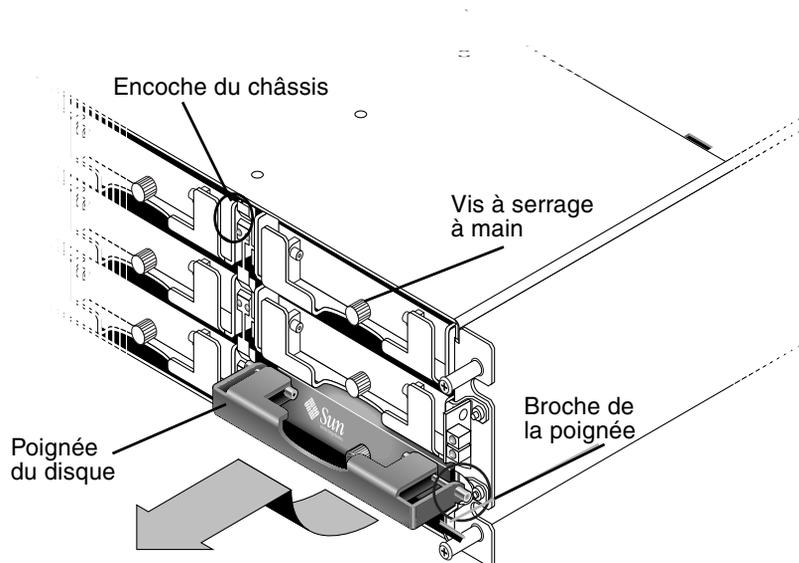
Vue de face d'un module de disque retiré du châssis
